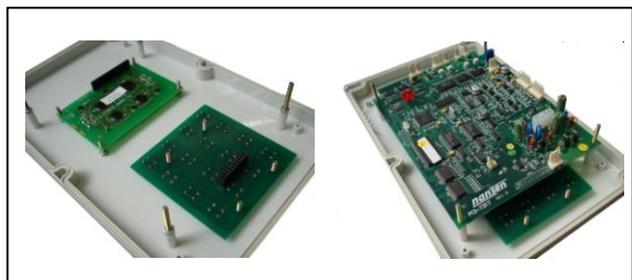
Display, Teclado e Placa Eletrônica Principal montada na parte de trás da tampa do Padrão de Energia.
